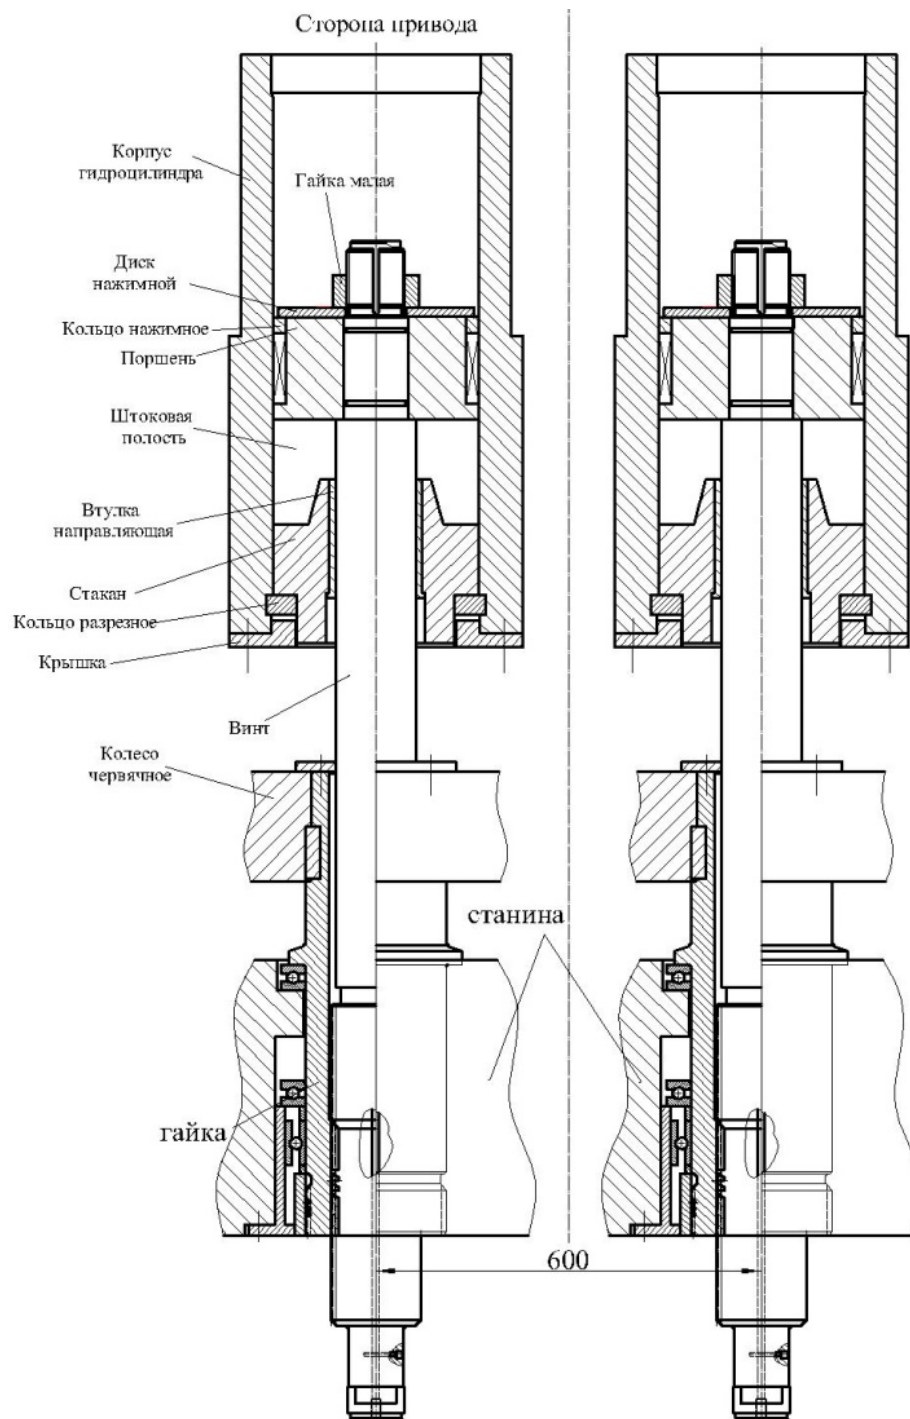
Схема механизма установки валков клетки 250 до реконструкции
